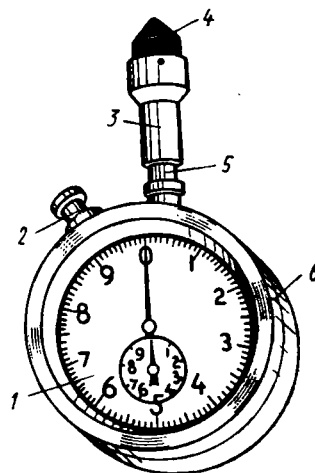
Часовой тахометр: 1 — циферблат, 2 — переключатель диапазонов, 3 — насадка, 4 — прижимная головка, 5 — вал, 6 — корпус
